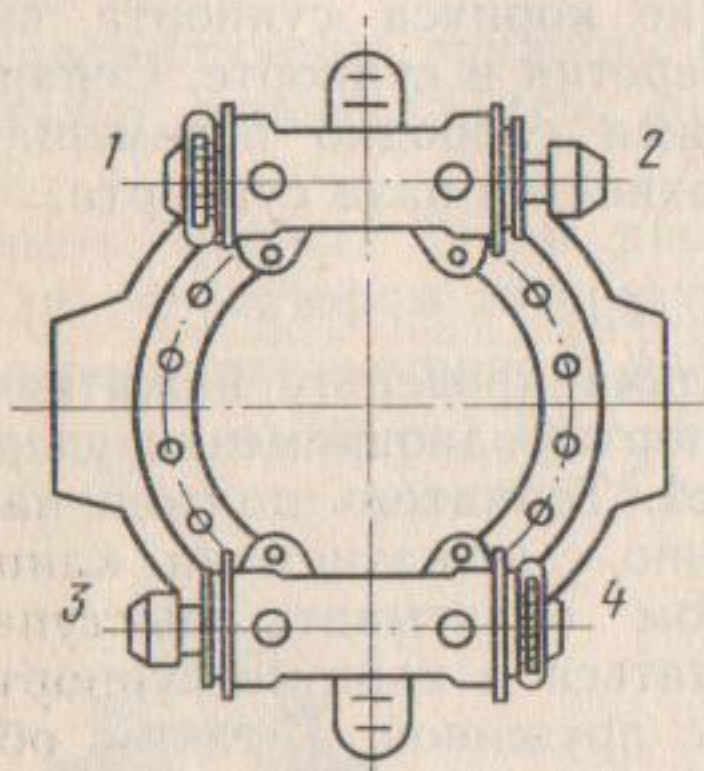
Схема расположения регулировочных винтов и втулок тормозного механизма переднего колеса:
